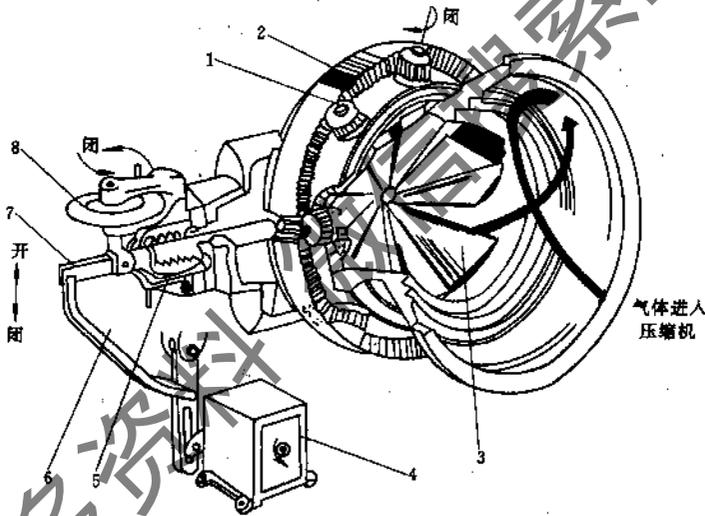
齿轮齿圈传动型式的压缩机进口可转导叶机构
